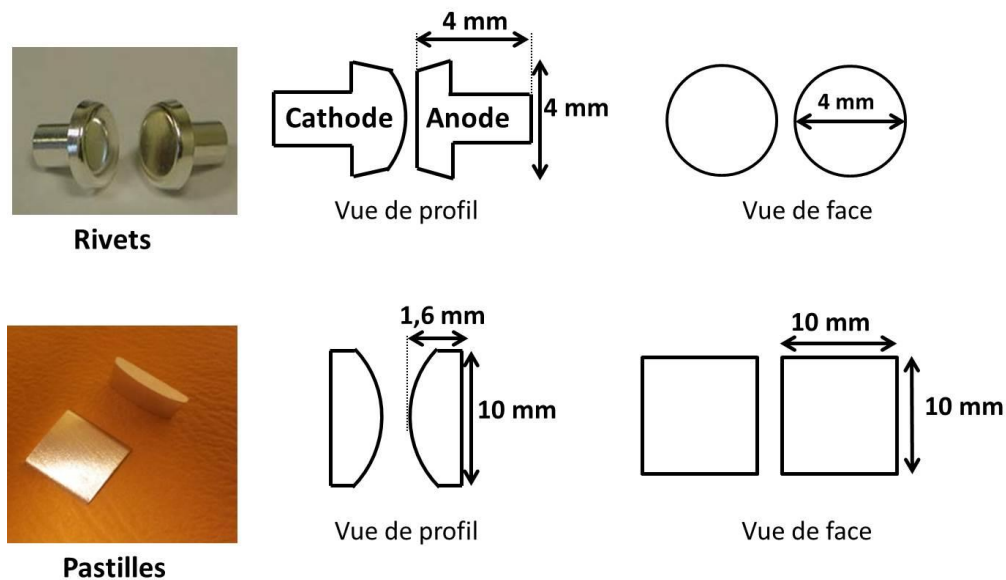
Formes des matériaux de contact : rivets et pastilles [14]
